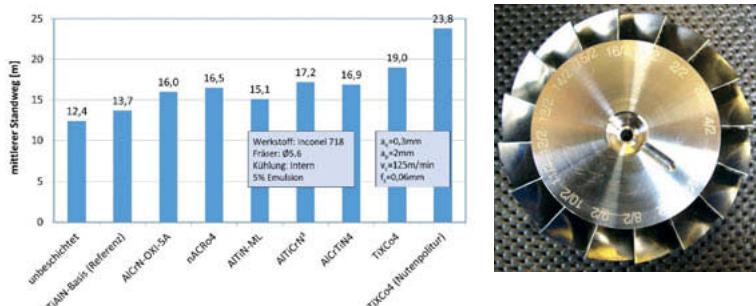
Standweg beim Fräsen von Inconel 718 mit unterschiedlich beschichteten Werkzeugen (links) sowie ein industriell bearbeitetes Bauteil (rechts)
